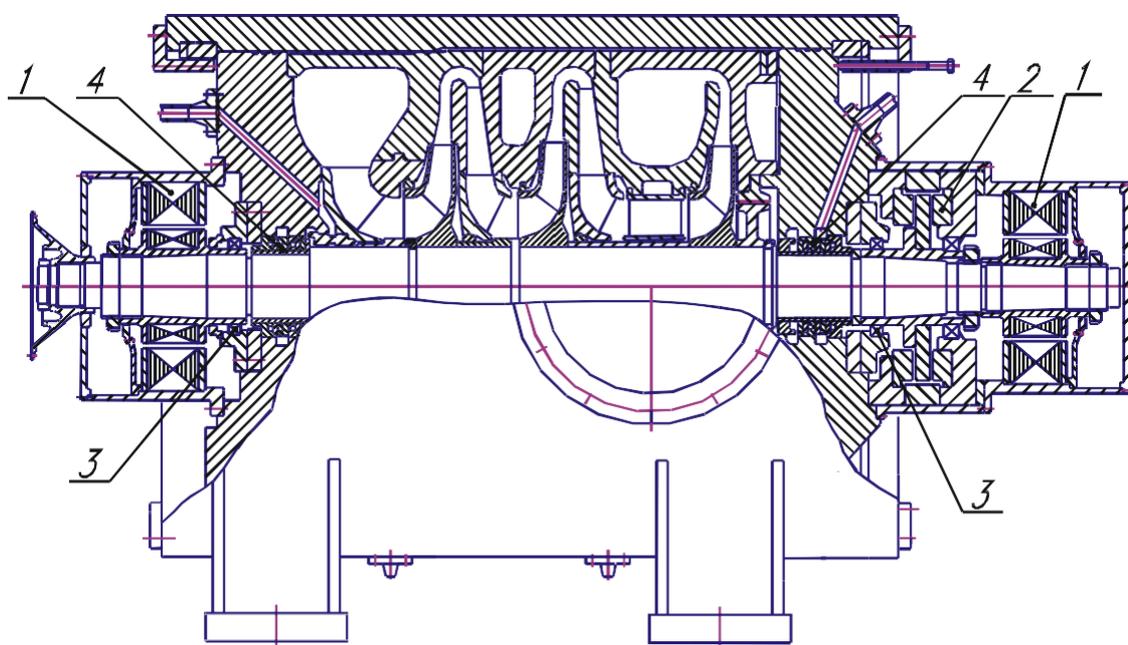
Трехступенчатый центробежный компрессор с вертикальным разъемом ГПА “Волга” конструкции НИИтурбокомпрессор
